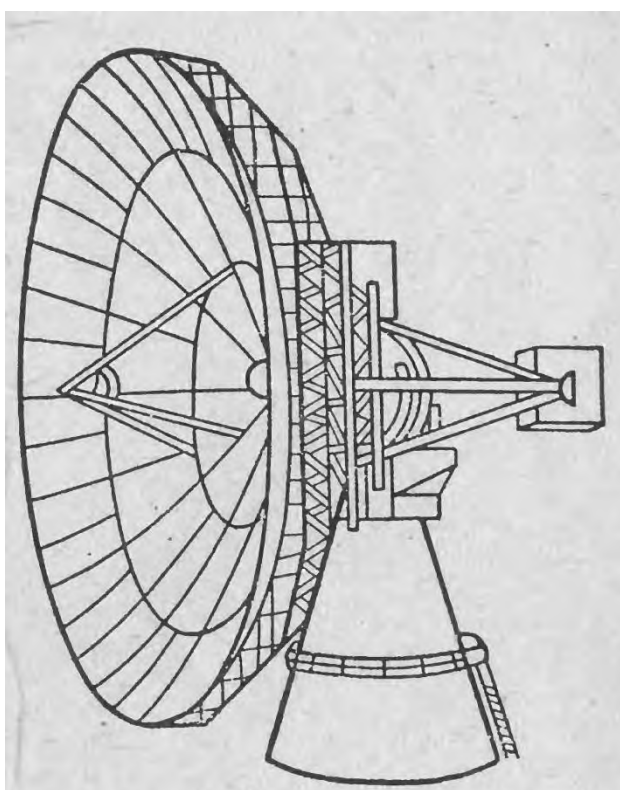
Опорно-поворотний пристрій з азимутально-кутовою підвіскою
